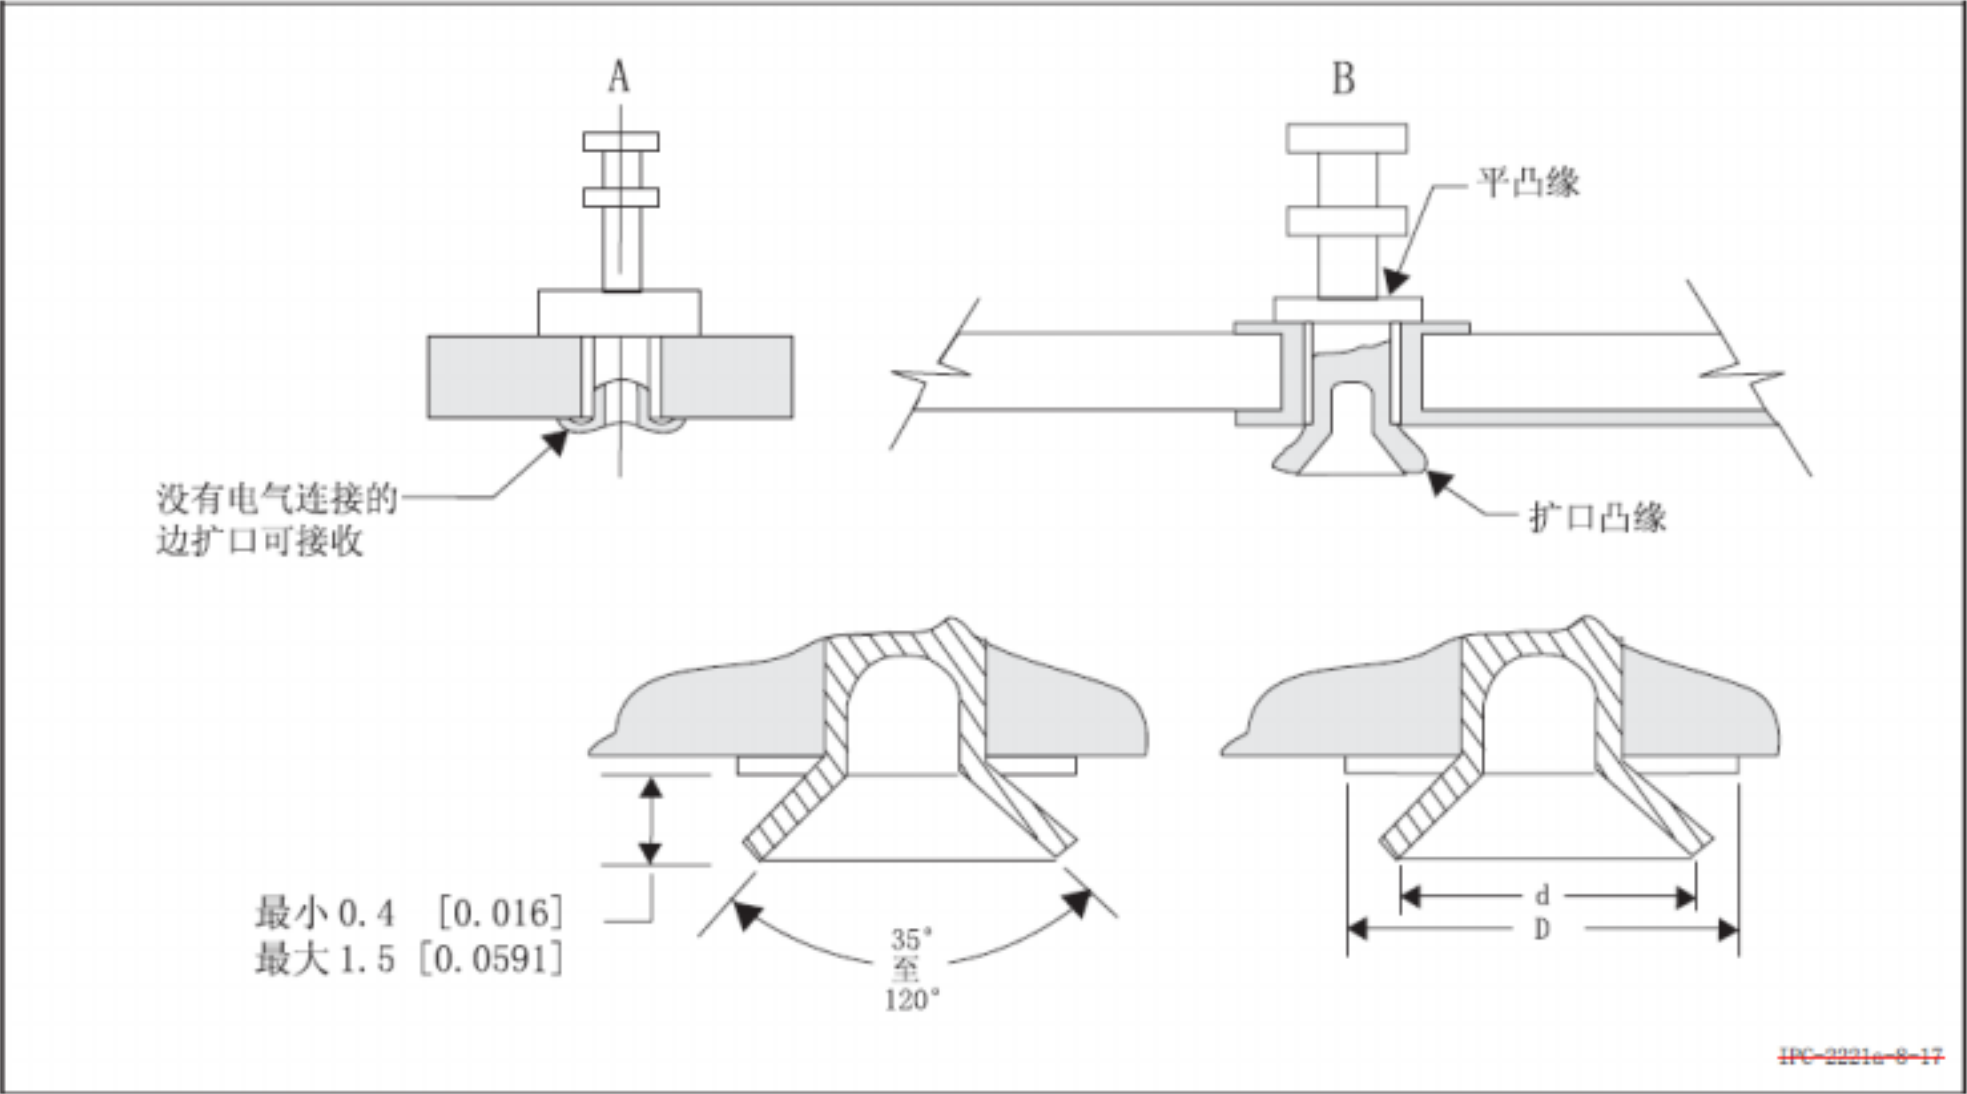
有支架的焊接柱组装、 mm[in] (IPC-2221A 图 8-17 有支架的焊接柱组装、 mm[in] , P67)
